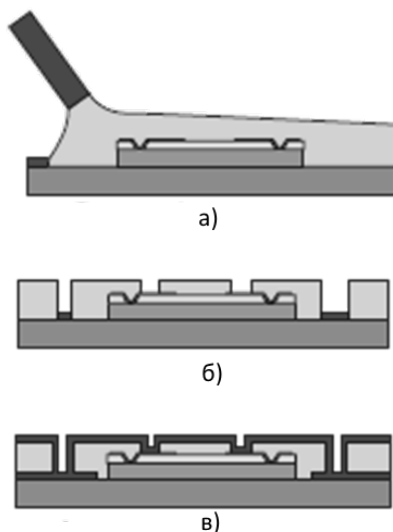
Соединение межсоединений кристалла ИС с платой аддитивным методом: а – заливка фоторезистом; б – проявление фоторезиста; в – аддитивная металлизация
